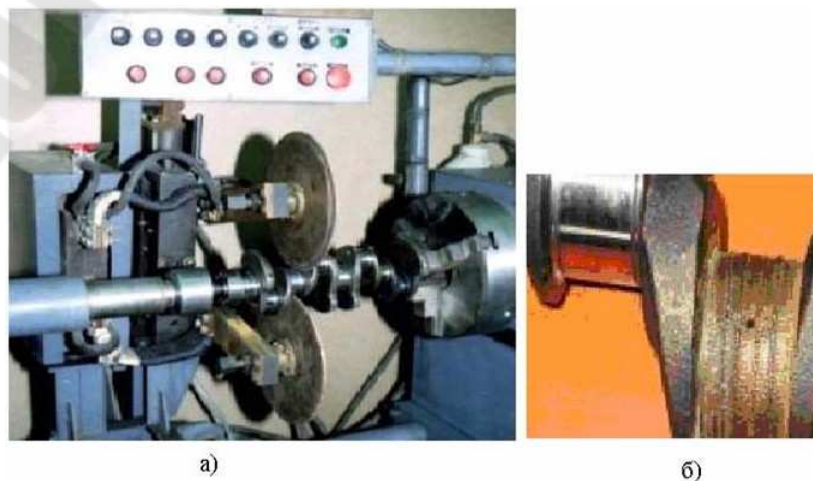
Схема электроконтактной наварки проволоки или ленты:
